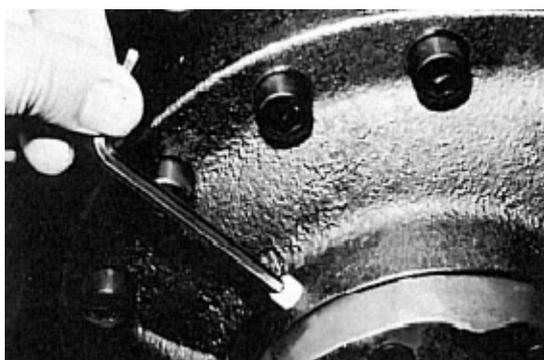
Vis borgne pour couvercle de palier, 160SUD & LUD
